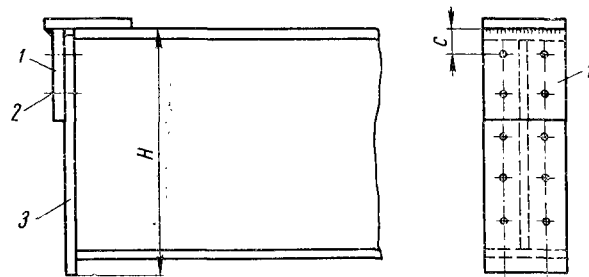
Установочный шаблон для сборки подкрановых балок
